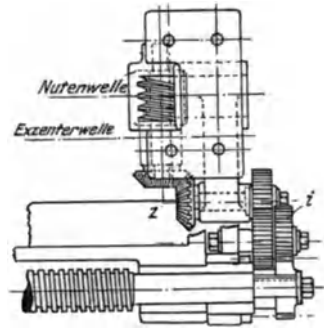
Der Antrieb für die Spiralen-Erzeugung.
